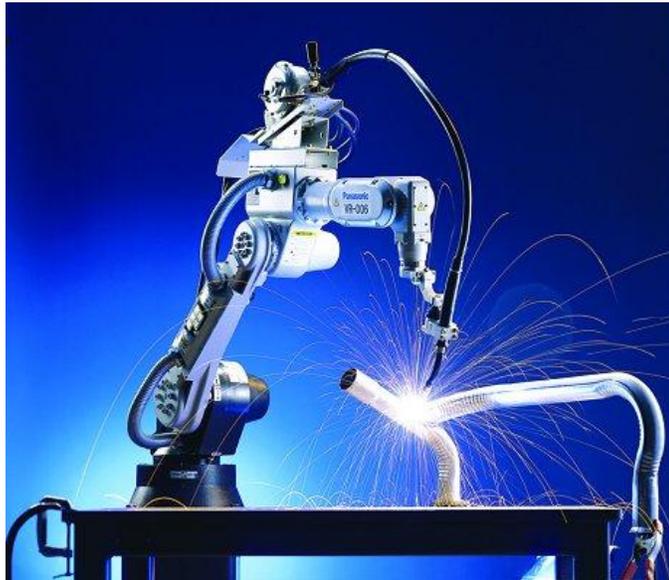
Soldadura robotizada (<http://www.interempresas.net/Robotica/FeriaVirtual/Producto-Robots-de-soldadura-Panasonic-91.html>)
